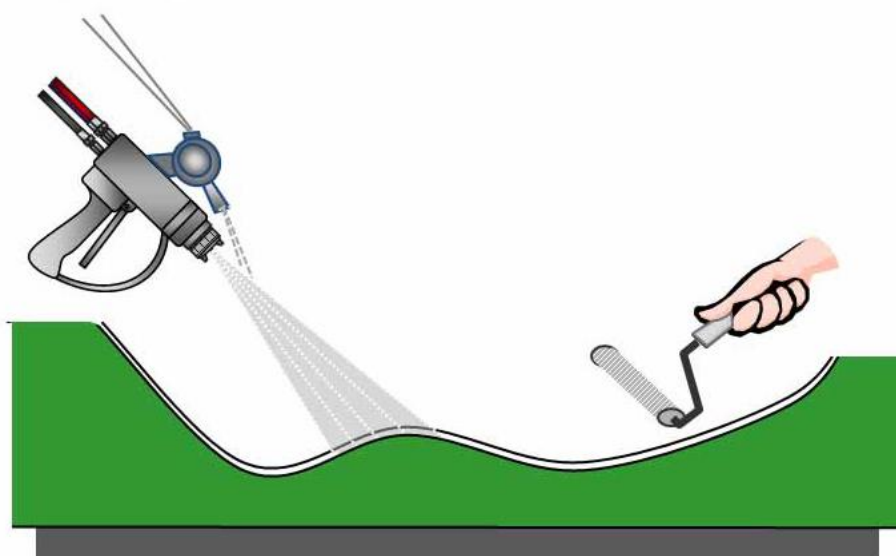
Esquema de um processo de moldagem por aspersão - FONTE: MOLDED FIBER GLASS (2013)
